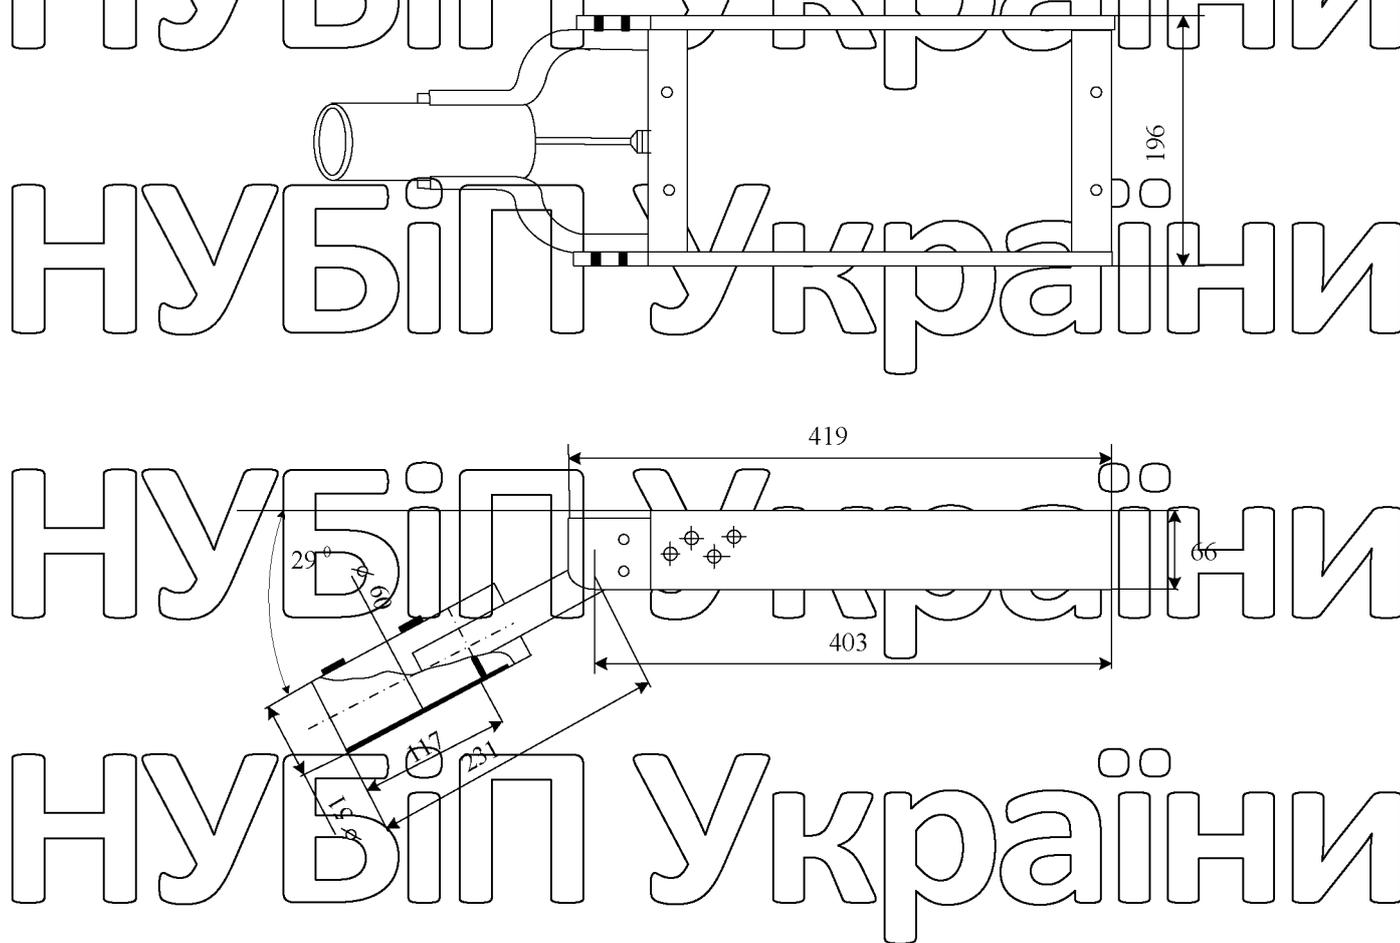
Зовнішній вигляд світильника LL-ДКУ-02-095-65Д
